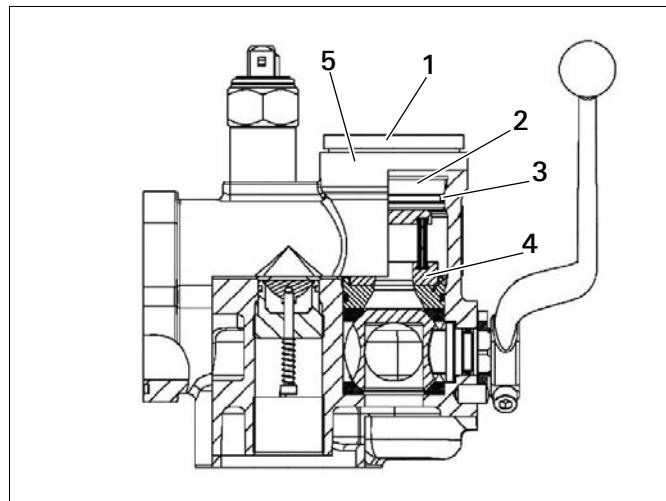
Testa del filtro con filtro di protezione (esempio)
